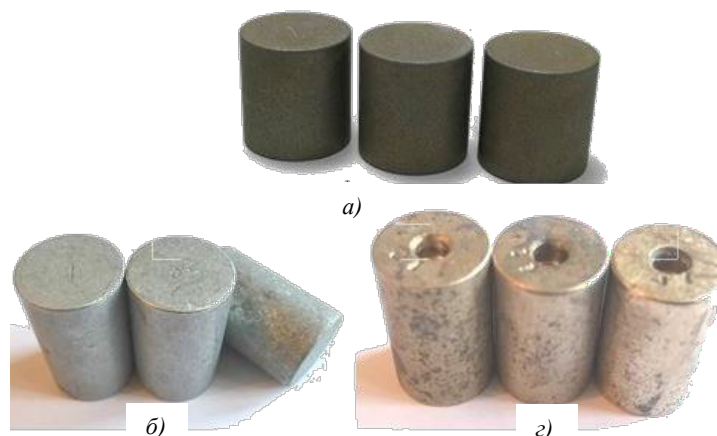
Образцы для определения съема металла с поверхности заготовки.
